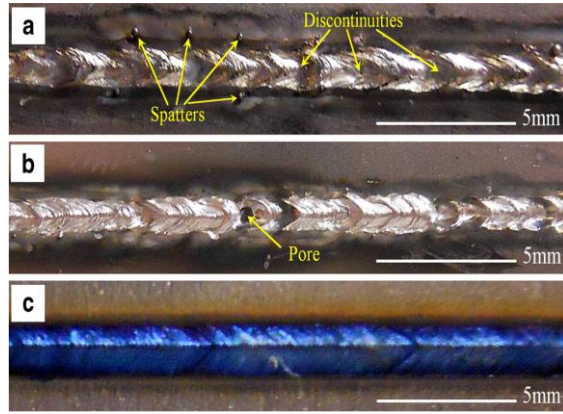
Q235低碳钢/5052铝合金的搭接接头形貌: a, b 不同工艺参数下单束激光焊接所获得的焊缝; c 双束激光焊接所获得的焊缝
